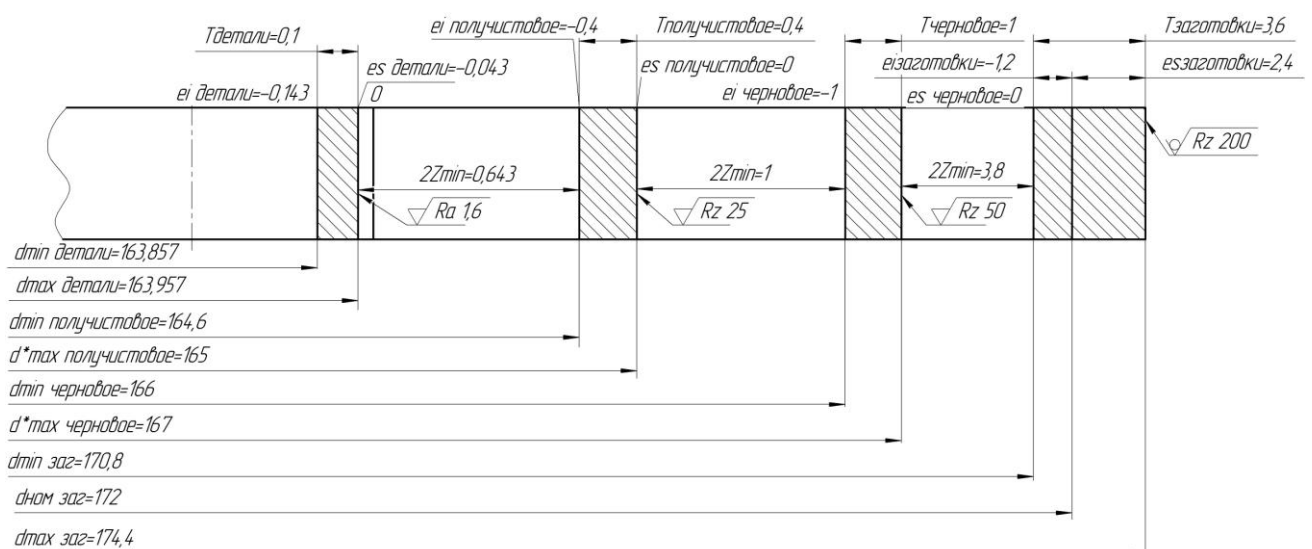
Схема расположения припусков и допусков для наружной цилиндрической поверхности  $\text{Ø}164\text{f9}(-0,043;-0,143)$
